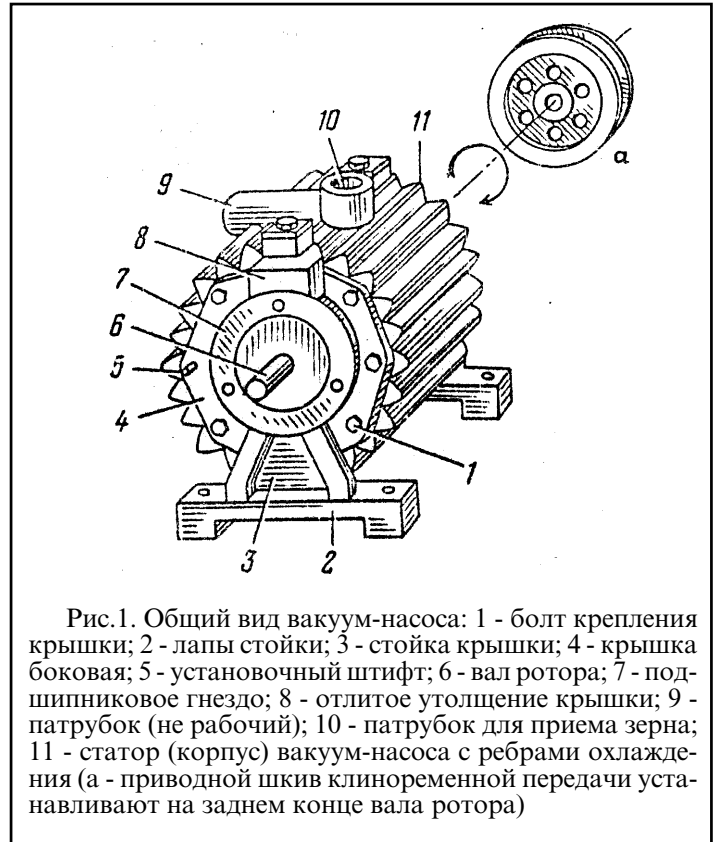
Общий вид вакуум-насоса: 1 - болт крепления крышки; 2 - лапы стойки; 3 - стойка крышки; 4 - крышка боковая; 5 - установочный штифт; 6 - вал ротора; 7 - подшипниковое гнездо; 8 - отлитое утолщение крышки; 9 - патрубок (не рабочий); 10 - патрубок для приема зерна; 11 - статор (корпус) вакуум-насоса с ребрами охлаждения (а - приводной шкив клиноременной передачи устанавливаются на заднем конце вала ротора)
